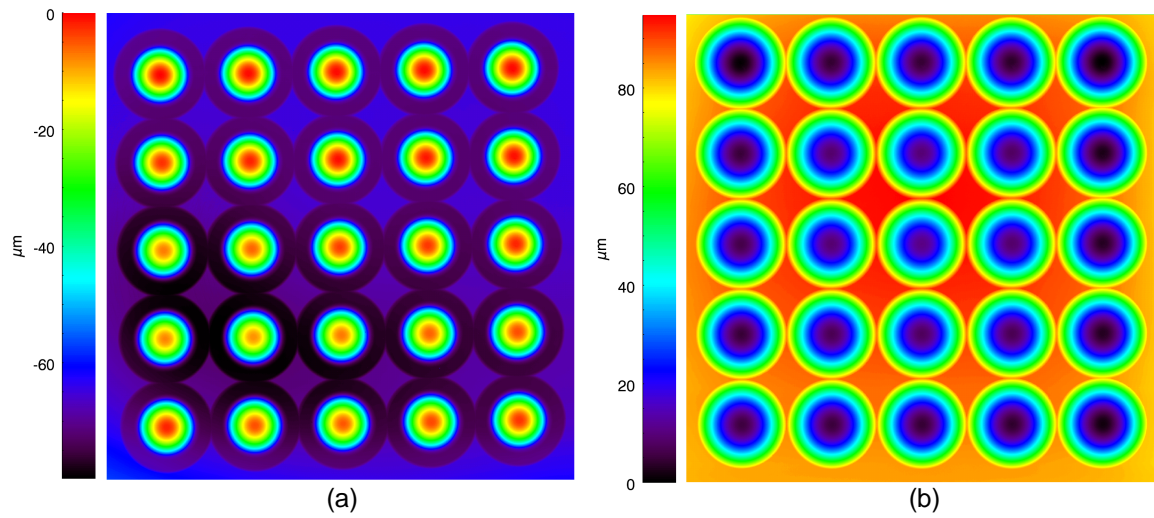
Cartographies de l'ensemble de la surface usinée des moules en aluminium, (a) moule pour microlentilles divergentes, (b) moule pour microlentilles convergentes.
